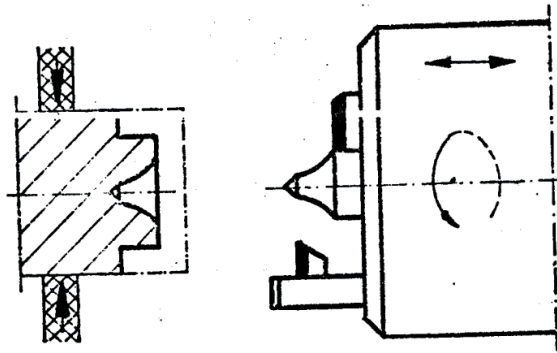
Faceamento, centragem e usinagem de diâmetro externo
